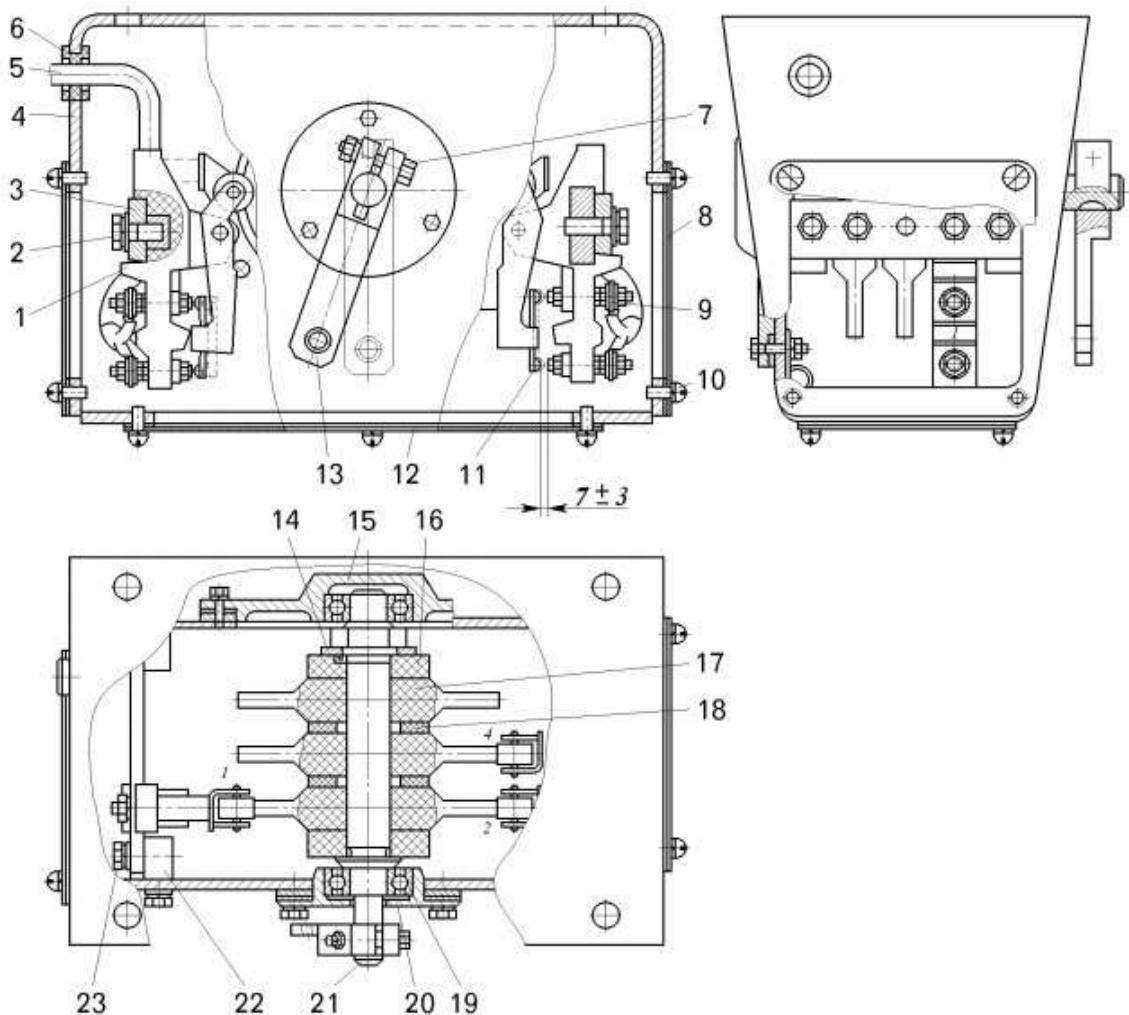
Ходовой контроллер: 1 – кулачковый элемент; 2, 7, 23 – болты; 3 – рейка; 4 – корпус; 5 – жгут проводов; 6 – уплотнительное кольцо; 8, 12 – крышки люков; 9 – контактный болт; 10 – винт; 11 – контактный мостик; 13 – рычаг; 14 – стопорная шайба; 15, 20 – крышки подшипников; 16 – кольцо; 17 – кулачковая шайба; 18 – изоляционная шайба; 19 – подшипник; 21 – вал кулачкового барабана; 22 – кронштейн
